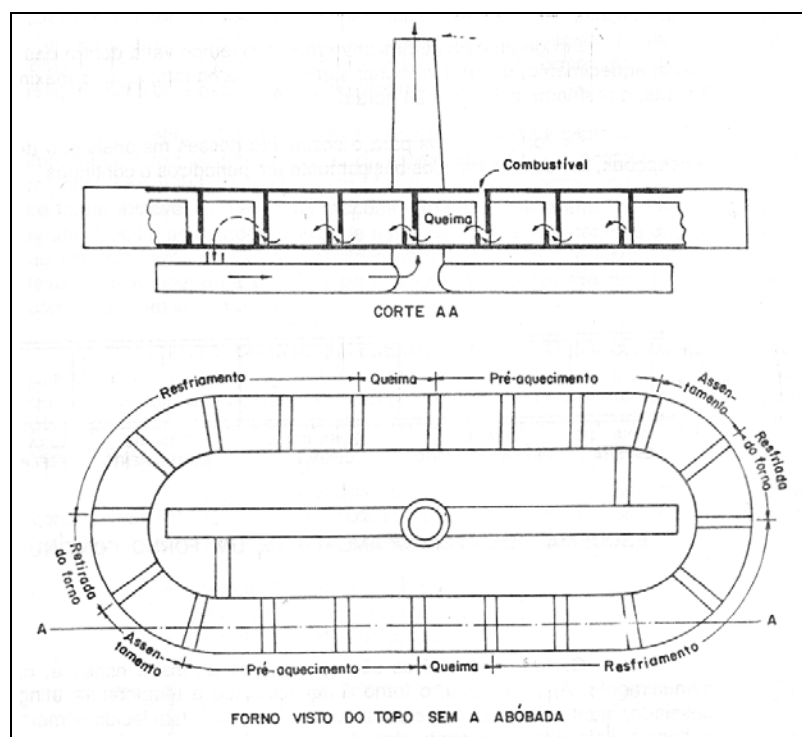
corte e planta baixa esquemáticos de forno tipo Hoffmann (fonte: SANTOS & SILVA, 1995).
